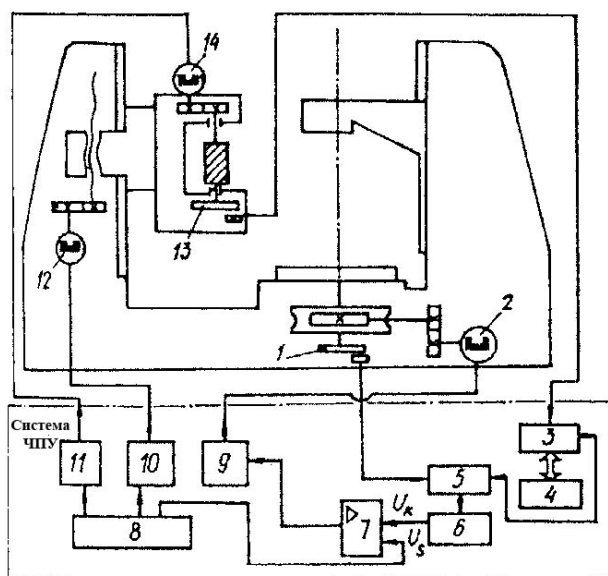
Структурная схема зубофрезерного станка с ЧПУ и разомкнутой кинематикой
